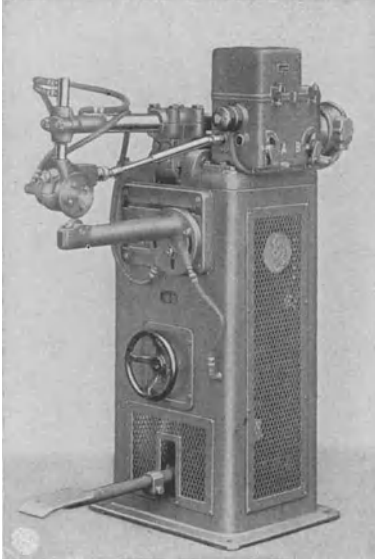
Nahtschweißmaschine mit Stromunterbrechung.
